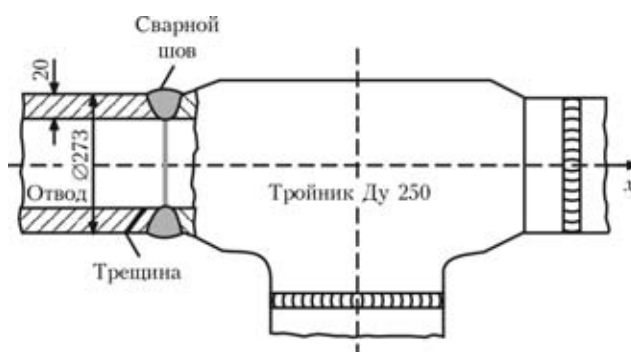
Схема трещины в сварном соединении отвода с тройником
